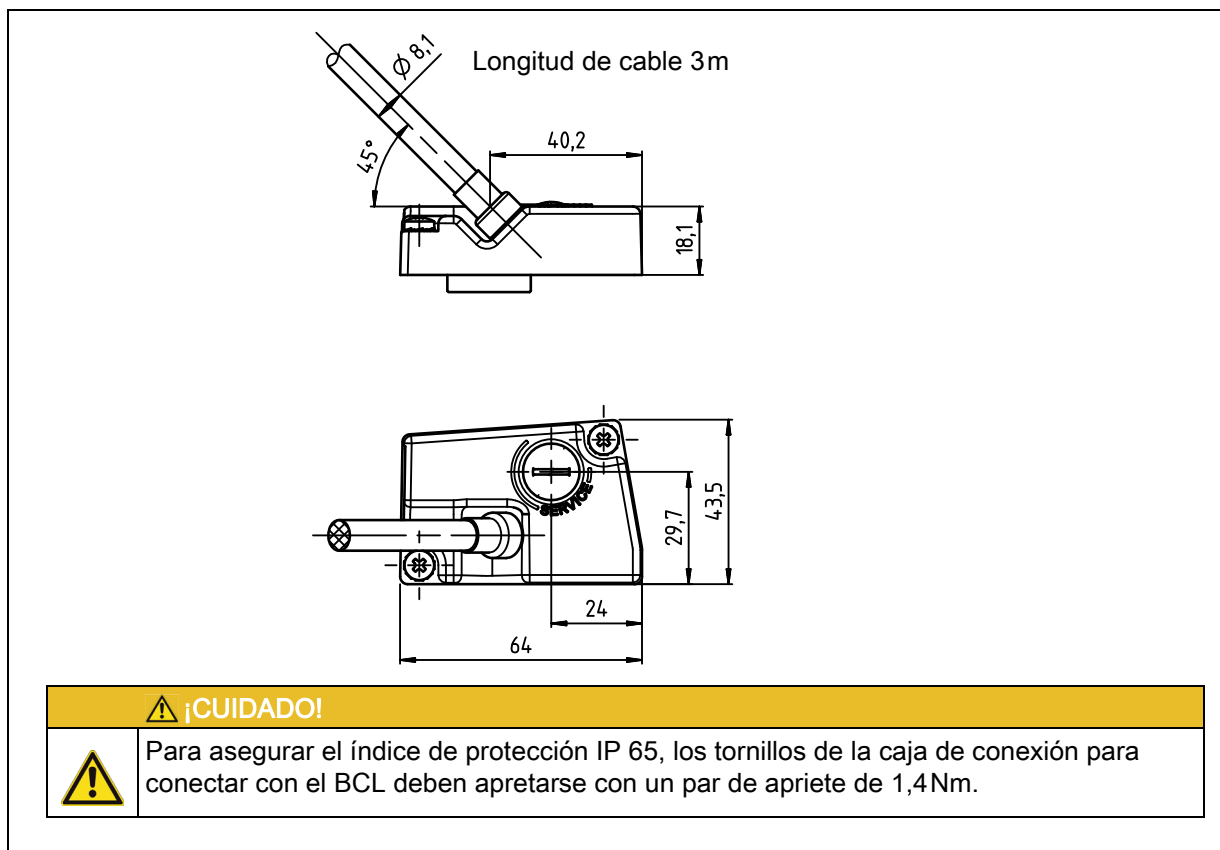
Dibujo acotado caja de cables KB 301-3000
